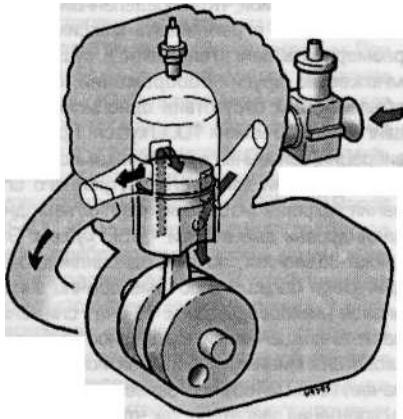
а Типичный одноцилиндровый двухтактный двигатель
